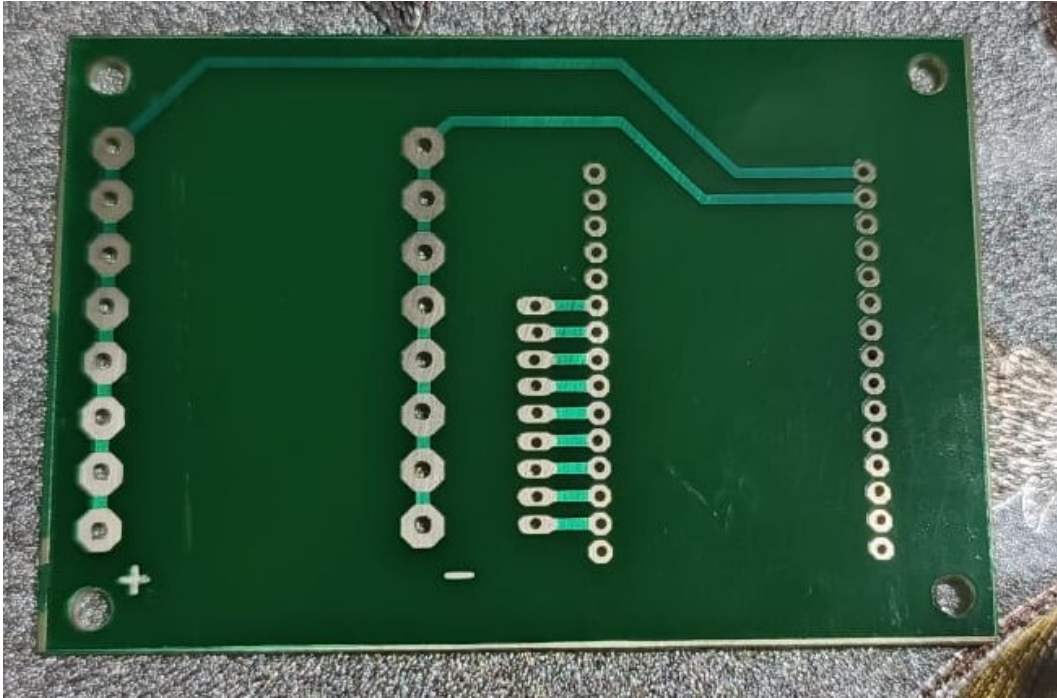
Pcb de fibra con antisolder. Fuente: Autores.
